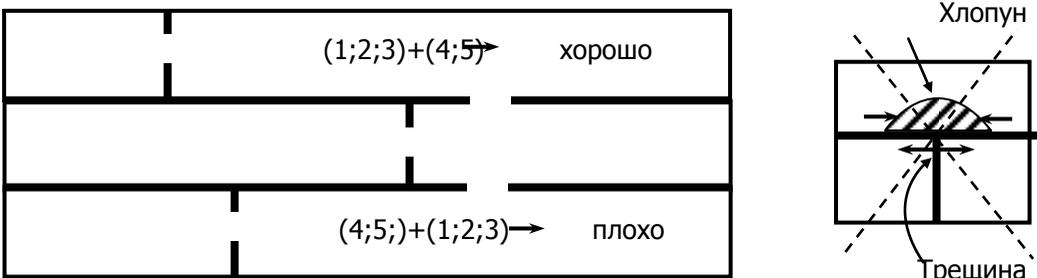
Последовательность выполнения сварных швов при сварке по-
